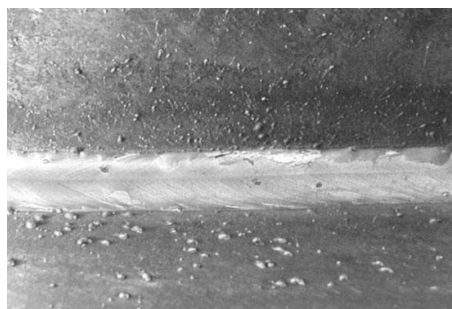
Сварное соединение при механизированной сварке в среде углекислого газа
